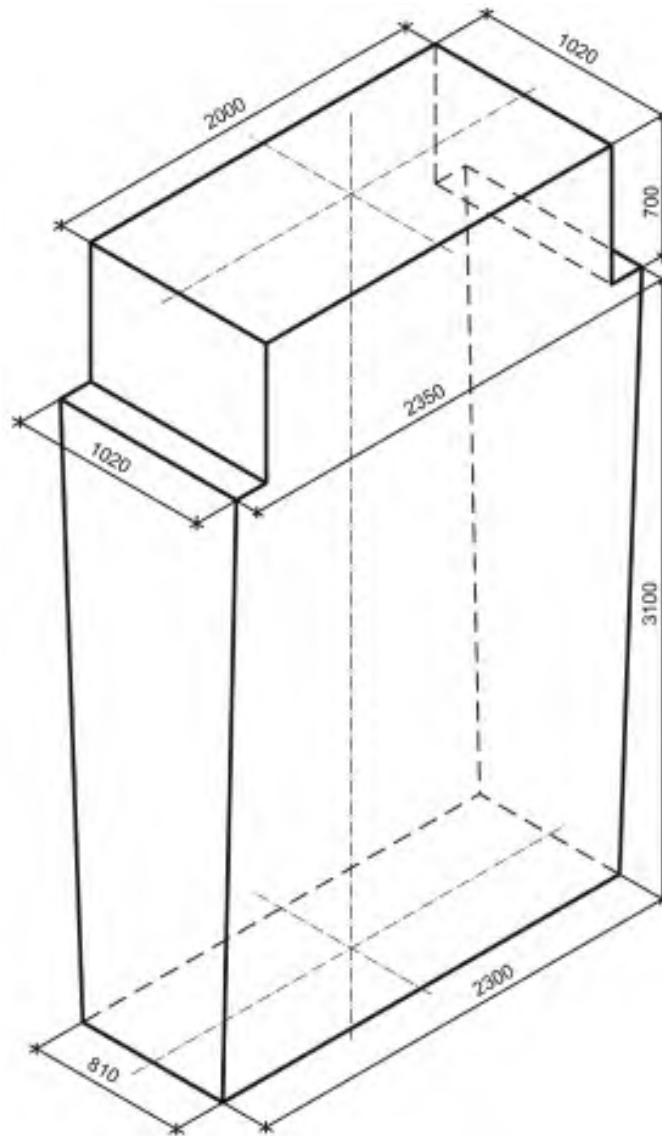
Геометричні розміри внутрішньої порожнини виливниці та прибуткової надставки для лиття 50-ти тонного листового зливка
